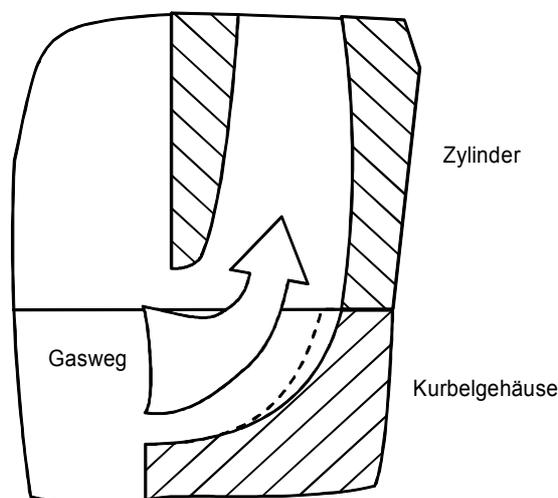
Schnitt durch Zylinder und Kurbelgehäuse längs des Überströmkanals
